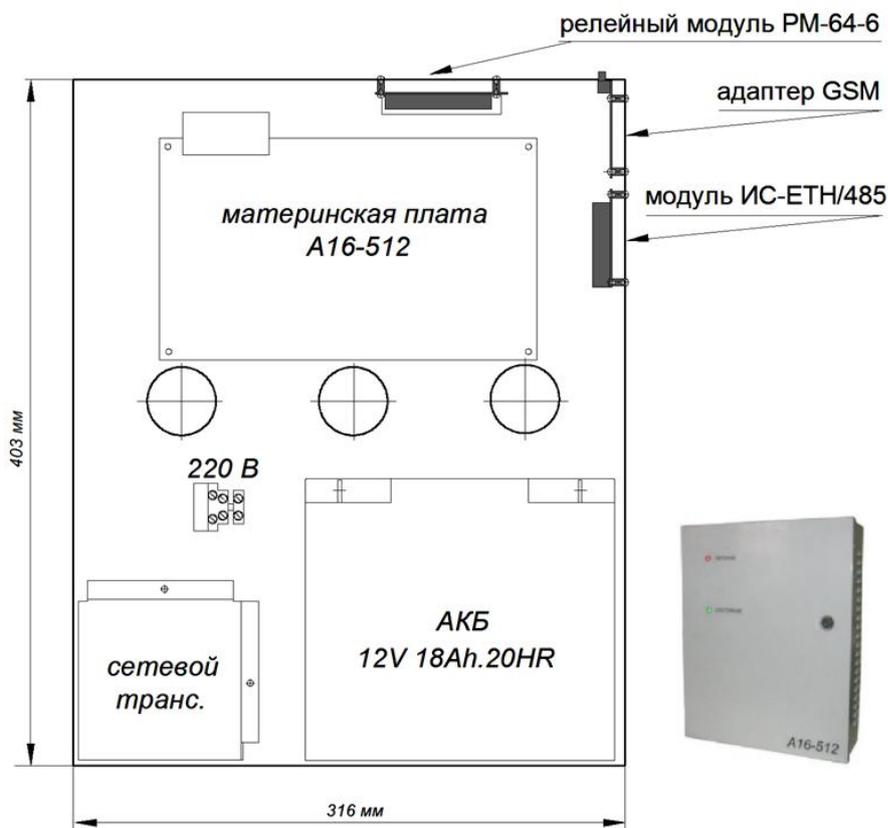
Внешний вид и эскиз основания корпуса ППКО
